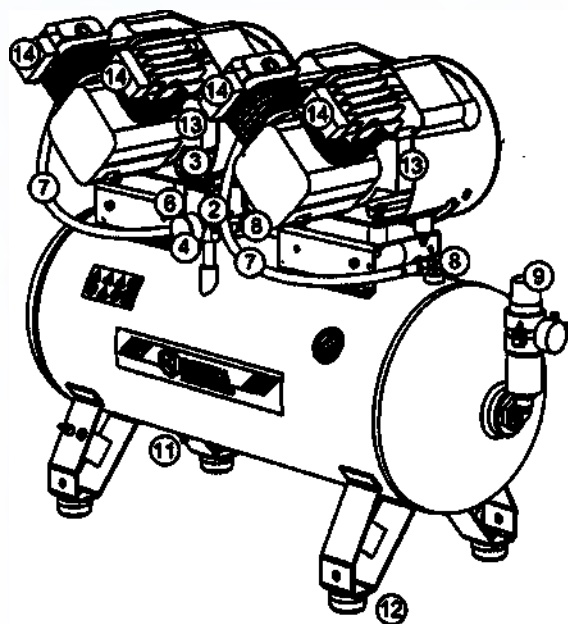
Общий вид компрессора KM-100.VS204T
